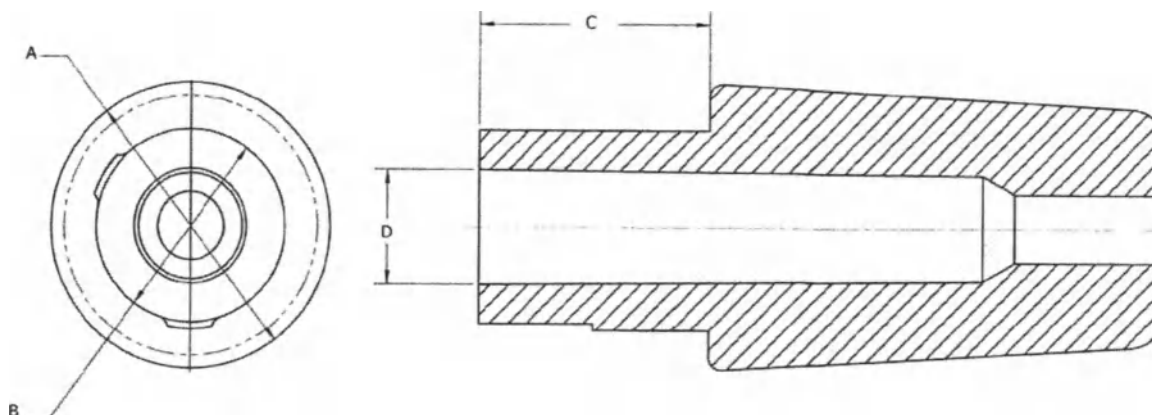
Соединитель разъема TRUE-LOCK, общий вид / Figure 9 – TRUE-LOCK Connector holder general view
